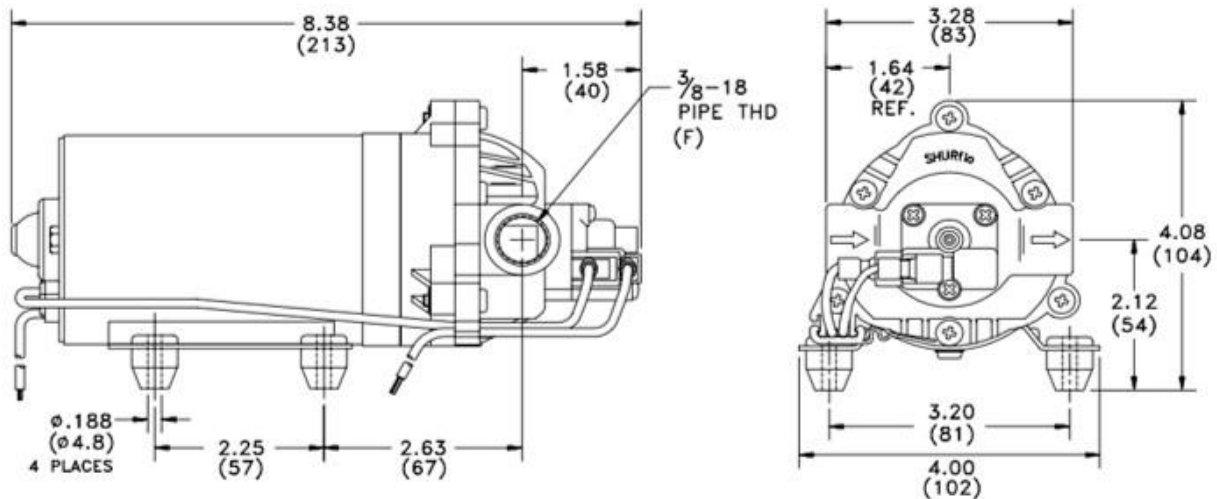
Disegni quotati della pompa SH-8000-543-23. Tra parentesi le dimensioni in mm
